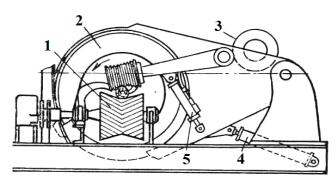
Конструктивный тип станков с позиционированием по центру бревна ротора перемещением на его балансирном рычаге: 1 — подающий конвейер; 2 — окорочная головка; 3 — двигатель; 4 — гидроцилиндр ротора; 5 — гидроцилиндр прижимного ролика
